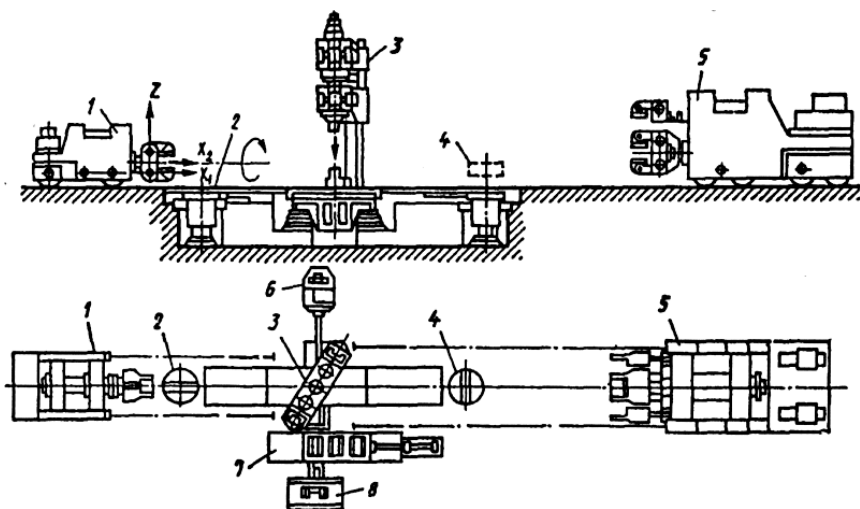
Схема расположения оборудования ковочного комплекса:
